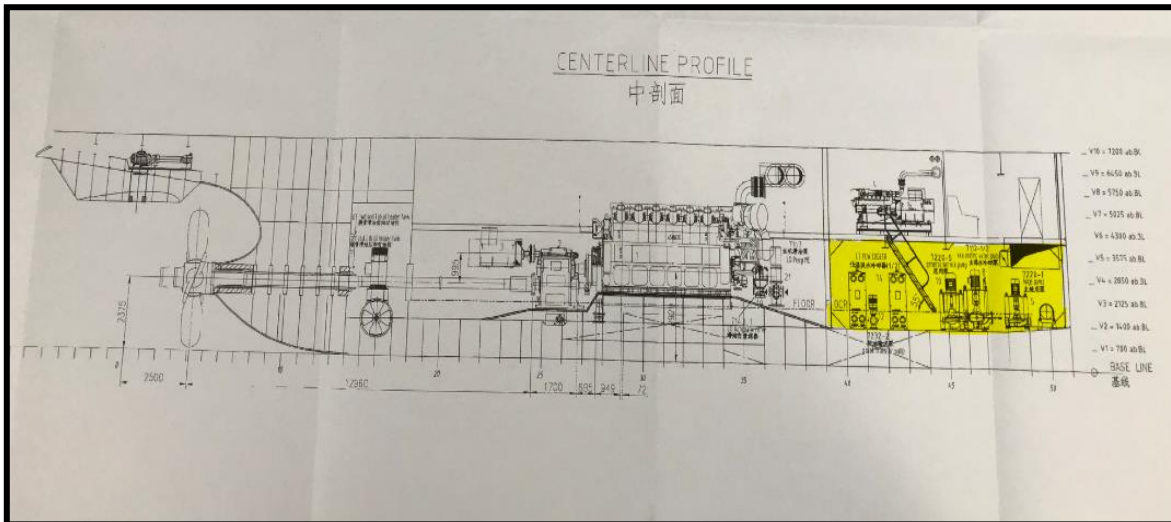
Plano costado sala de máquinas OPDR ANDALUCÍA.
